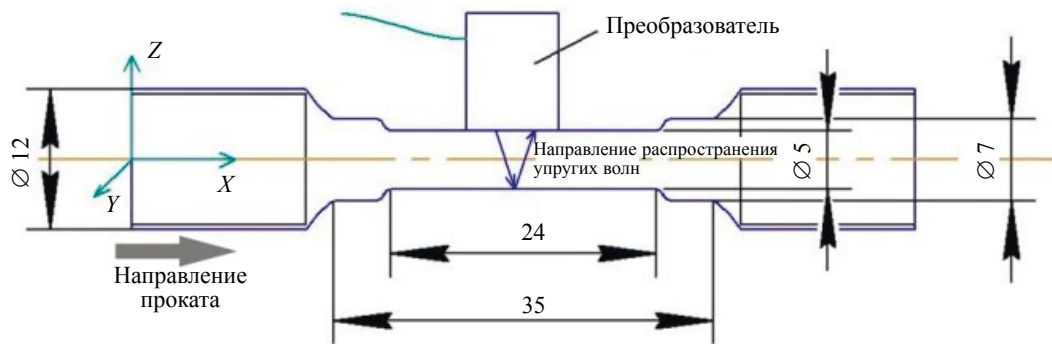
Образец для усталостных испытаний и схема установки преобразователей.
